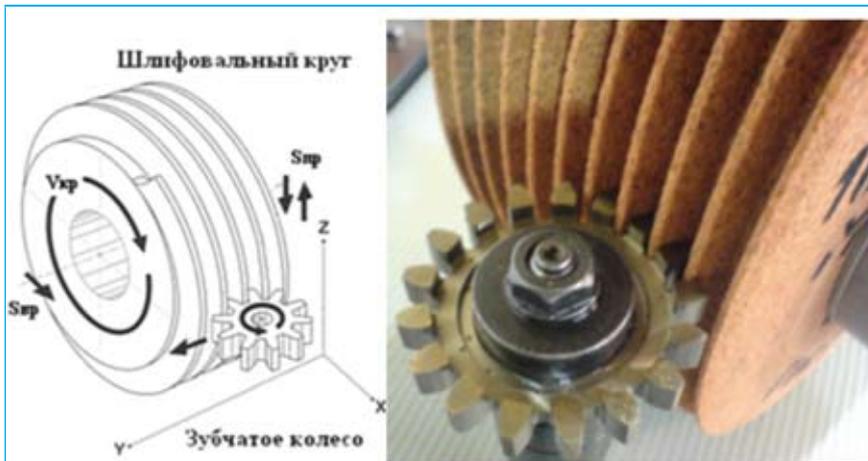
Шлифование зубчатых колес по схеме непрерывного обката.
